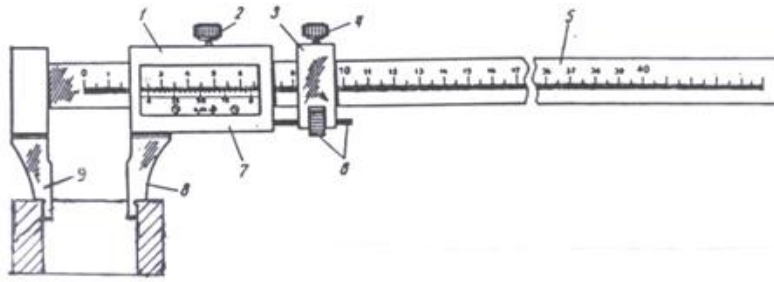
Конструкция штангенциркуля ШЦ-III:
